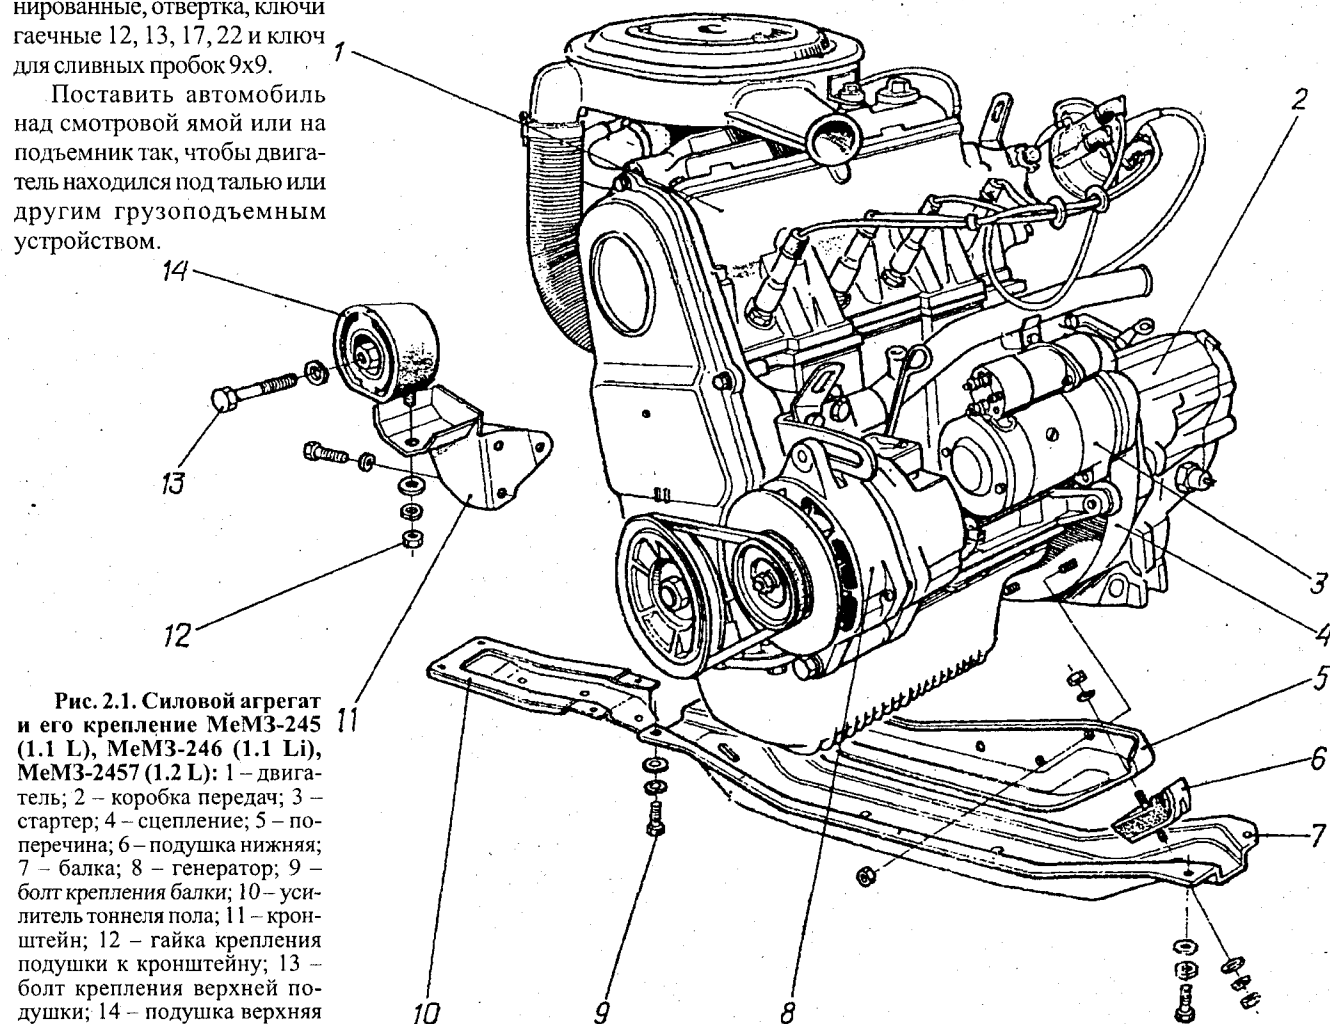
Силовой агрегат и его крепление MeMZ-245 (1.1 L), MeMZ-246 (1.1 Li), MeMZ-2457 (1.2 L): 1 – двигатель; 2 – коробка передач; 3 – стартер; 4 – сцепление; 5 – поперечина; 6 – подушка нижняя; 7 – балка; 8 – генератор; 9 – болт крепления балки; 10 – усилитель тоннеля пола; 11 – кронштейн; 12 – гайка крепления подушки к кронштейну; 13 – болт крепления верхней подушки; 14 – подушка верхняя
